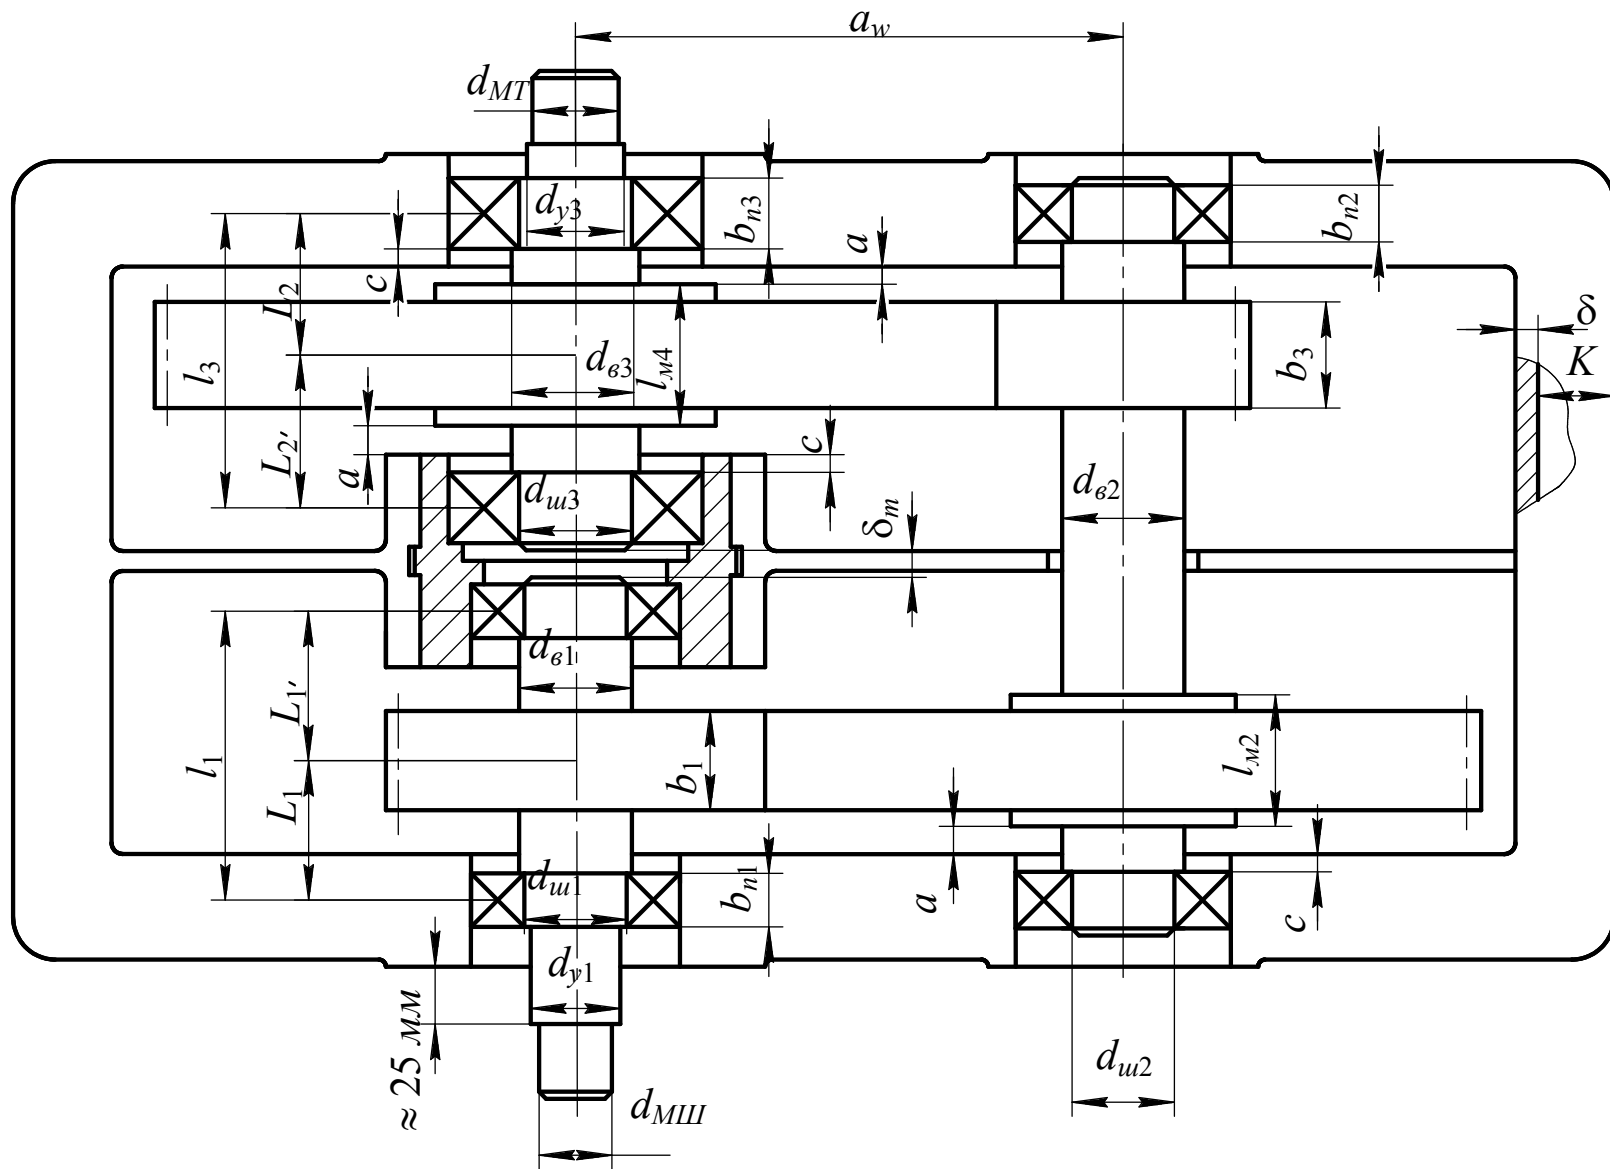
Эскизная компоновка двухступенчатого цилиндрического редуктора с входным и выходным валами, оси которых совпадают
